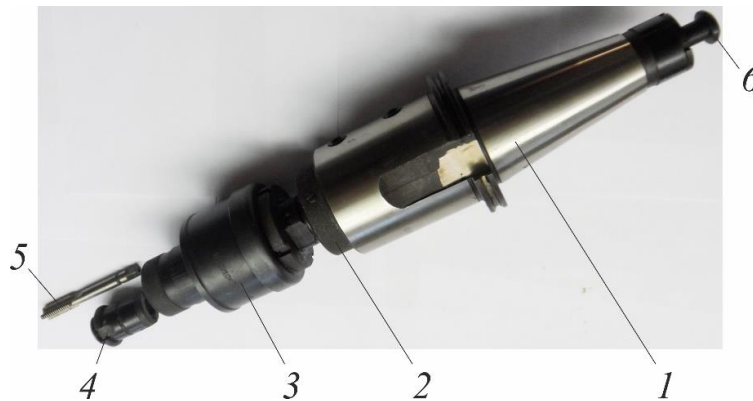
АСП для нарезания резьбы метчиками: 1 – базисный агрегат; 2 – регулировочная гайка; 3 - резьбонарезной патрон; 4 – вставка для закрепления метчика; 5 - метчик
